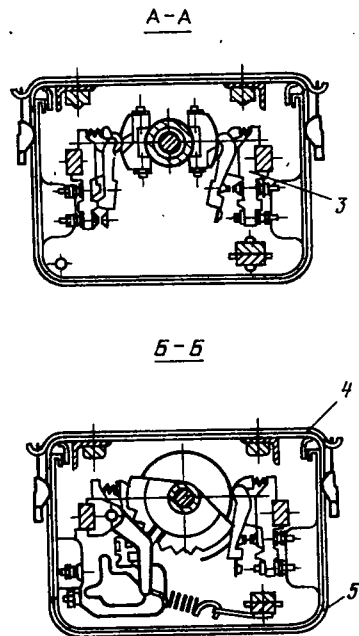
Общий вид кулачкового контроллера КВ-70
